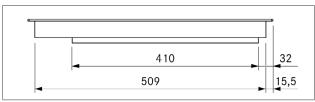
Dimensões do aparelho PKI3, vista lateral
